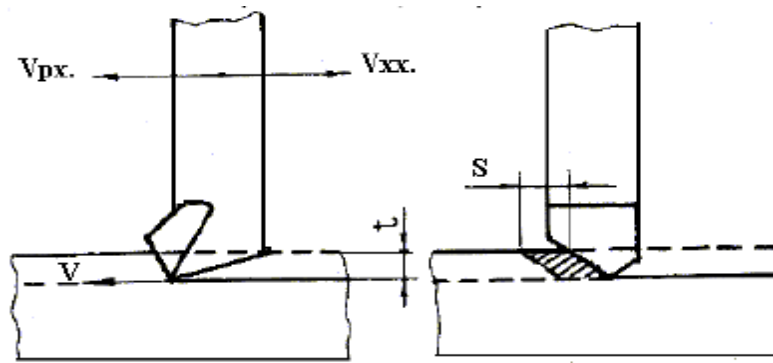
Схема срезания припуска строгальным резцом:
